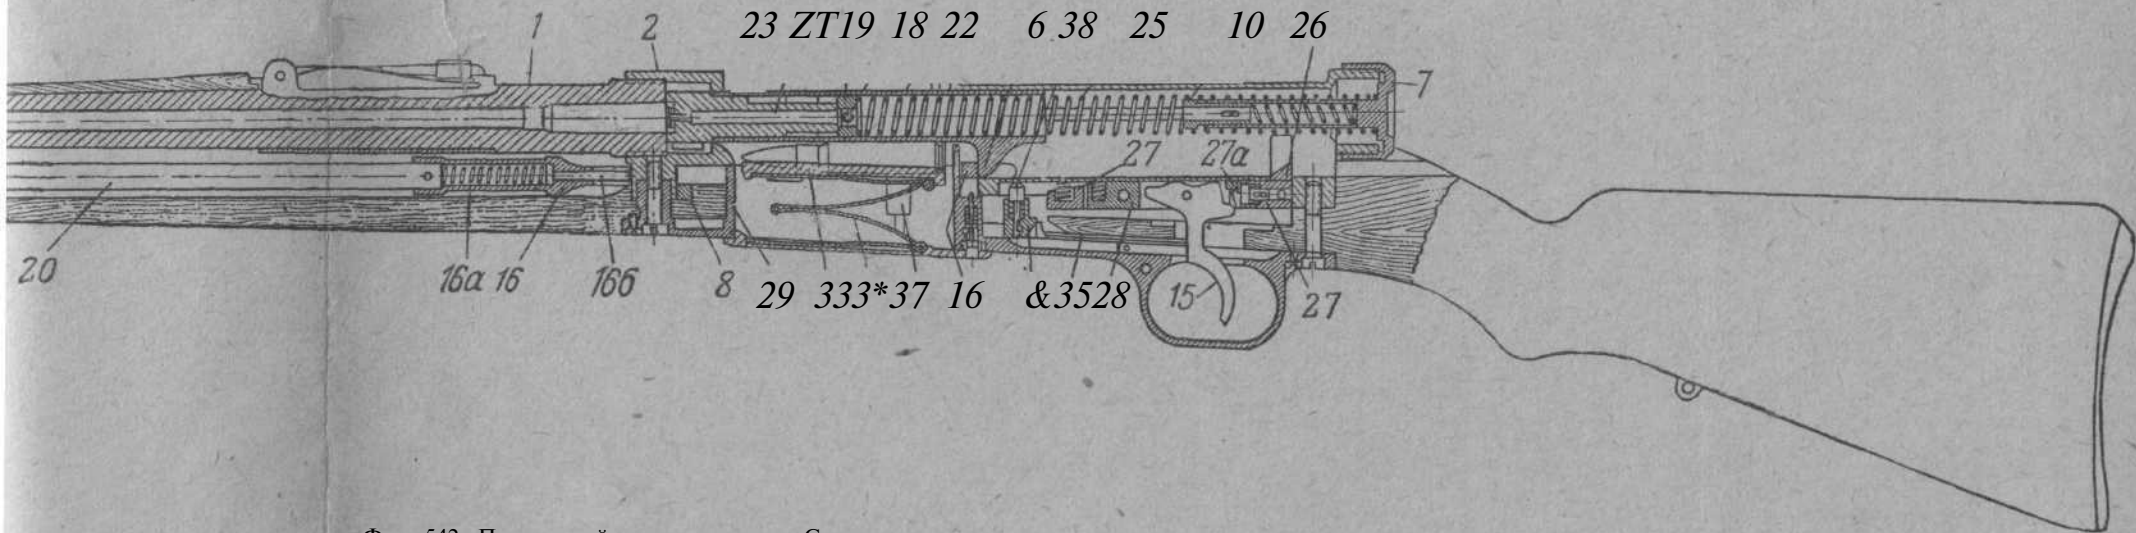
Вид винтовки ЗН-29 (затвор заперт),
